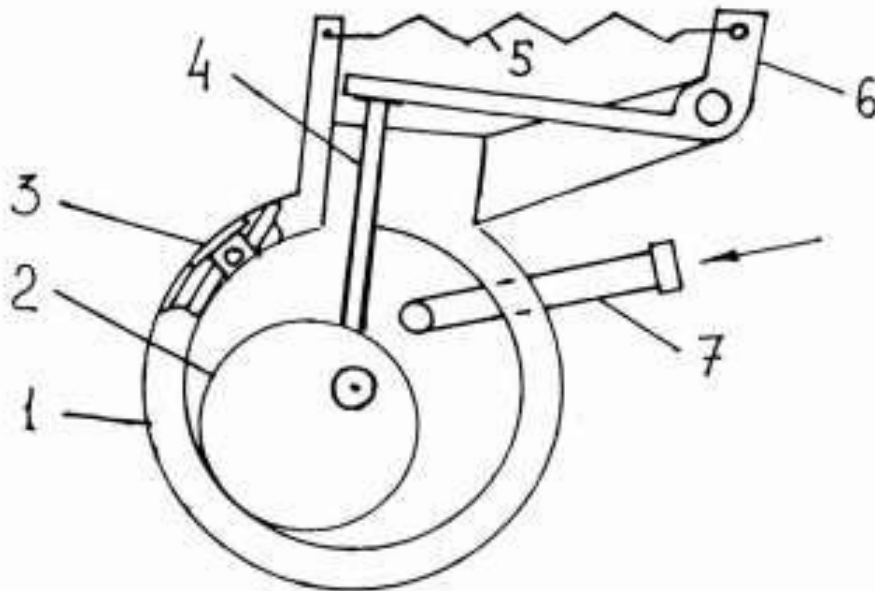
Схема вакуумного насоса з ротором, що котиться: 1 – корпус; 2 – ротор; 3 – вихлопний клапан; 4 – пластина; 5 – пружина; 6 – важіль; 7 – всмоктувальний патрубок.
